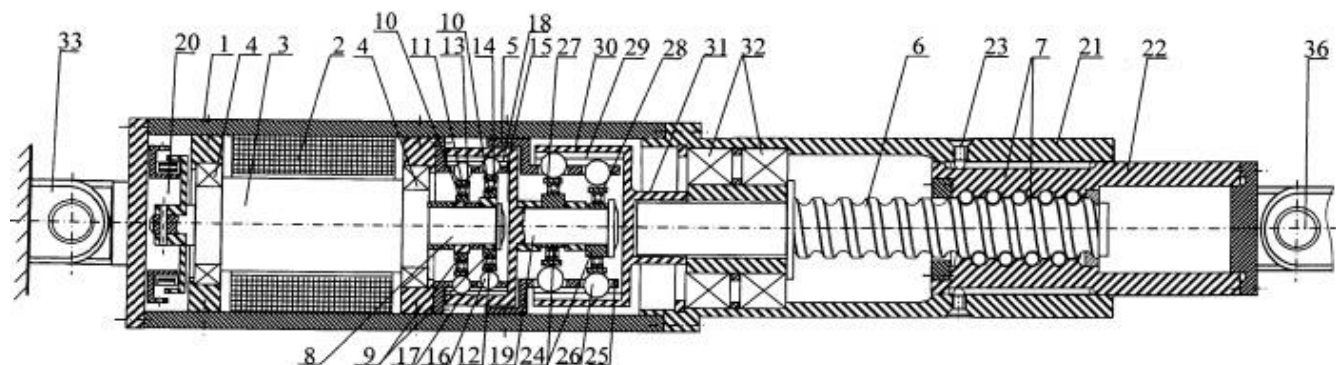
Схема приводу з двома послідовними хвильовими редукторами: Рис. 3.2.1. Схема приводу: 1 – корпус; 2 – електродвигун; 3 – ротор; 4 – підшипники; 5 – хвильовий редуктор; 6 – гвинт; 7 – шарико-гвинтовий механізм; 8 – вал ротора; 9, 24 – хвильоутворювач; 10 – ексцентрики; 11, 12, 32 – підшипники; 13, 14, 27, 28 – робочі кільця; 15, 25 – сепаратор; 16, 26 – тіла обертання; 17, 30 – жорстке колесо; 18, 29 – хвильова поверхня; 19, 31 – вал; 20 – датчик положення вала; 21 – корпус; 22 – штовхач; 23 – стопор.
